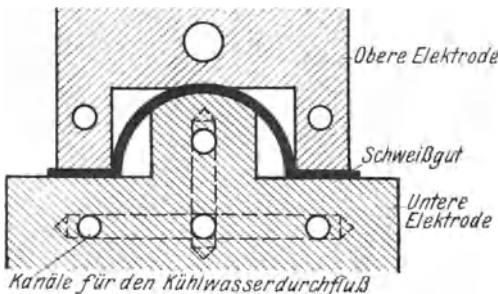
Elektroden (Klemmbacken) einer Profileisenschweißmaschine.
